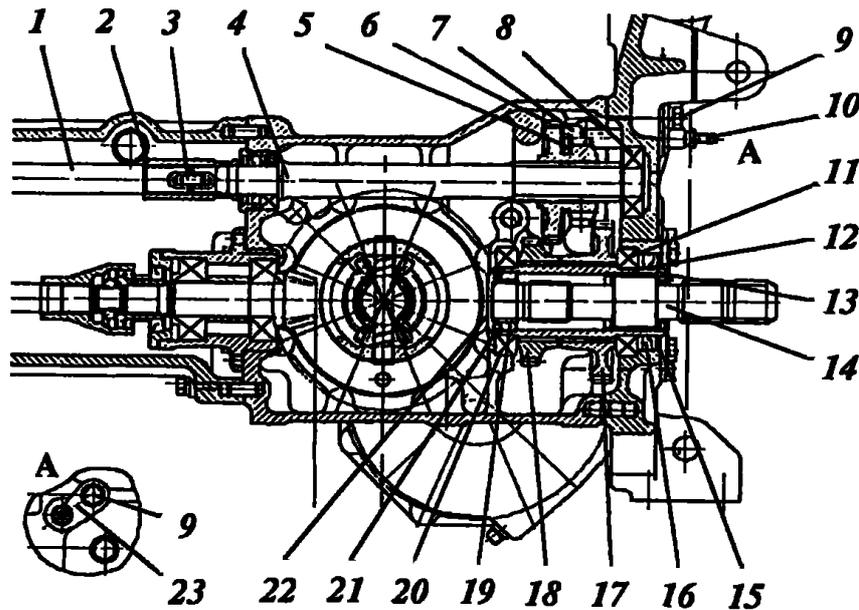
Задний ВОМ: 1, 4, 12 - валы; 2 - втулка; 3, 7, 21 - штифты; 5 - вилка; 6 - блок-шестерня; 8, 20 - подшипники; 9 - болт; 10 - валик; 11, 13 - кольца стопорные; 14 - хвостовик; 15 - плита; 16 - манжета; 17, 18 - шестерни; 19 - кольцо; 22 - заглушка; 23 - пластина
